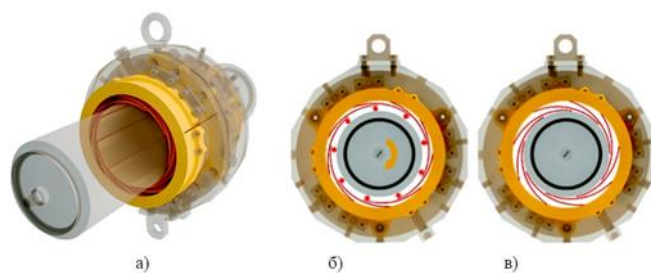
Типичная конструкция лепесткового газодинамического подшипника: а – общий вид; б – подшипник в рабочем состоянии; в – подшипник при неподвижном вале
